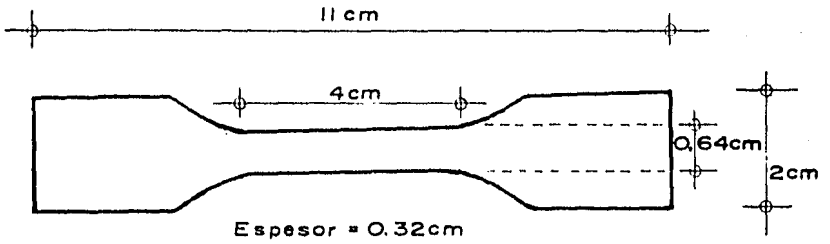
ESPECIMEN PARA ENSAYE A LA TENSION.
